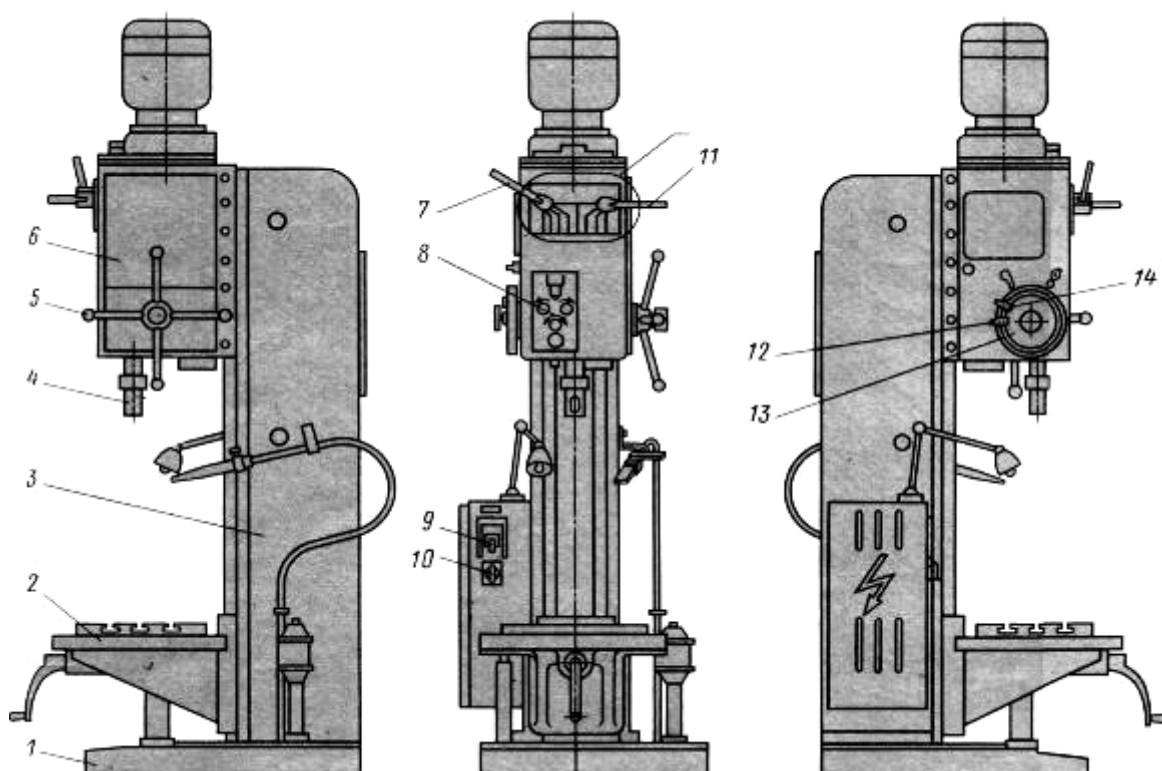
Общий вид вертикально-сверлильного станка модели 2H125:
